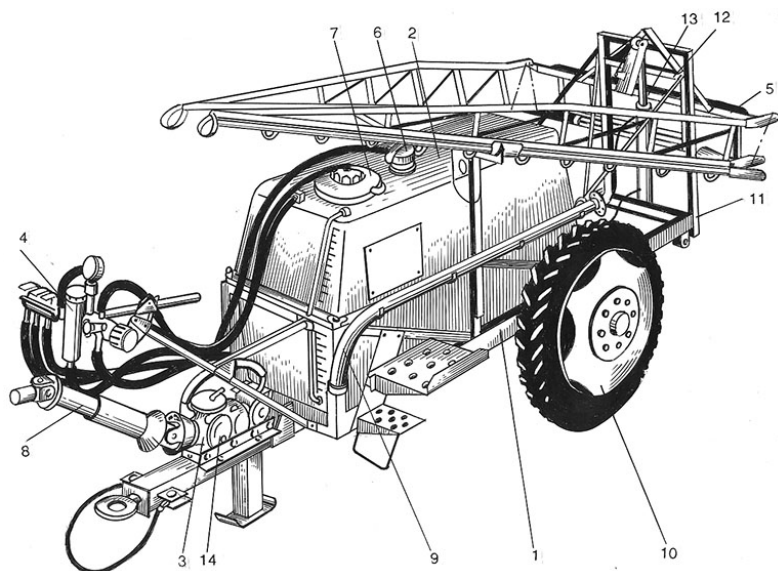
Общий вид прицепного штангового опрыскивателя: *1* – рама; *2* – бак; *3* – насосный агрегат; *4* – распределитель с регулятором давления; *5* – штанга; *6* – всасывающий фильтр; *7* – смеситель; *8* – карданный вал; *9* – заправочный рукав; *10* – колесо; *11* – рамка; *12* – ползун; *13* – гидроцилиндр; *14* – сливная пробка
